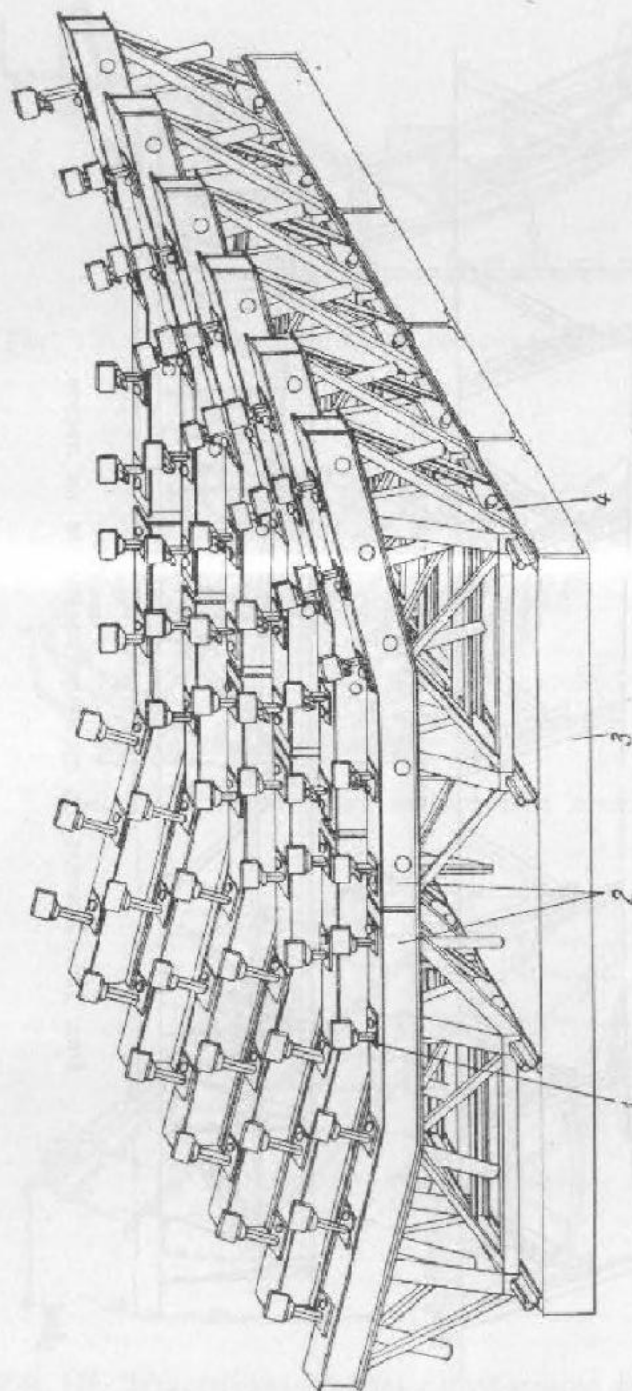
Универсальная постель для сборки и сварки секций.
